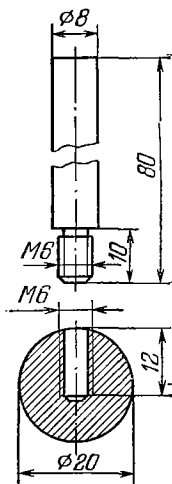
Приспособление для изготовления ультразвуковой линзы из оргстекла.
